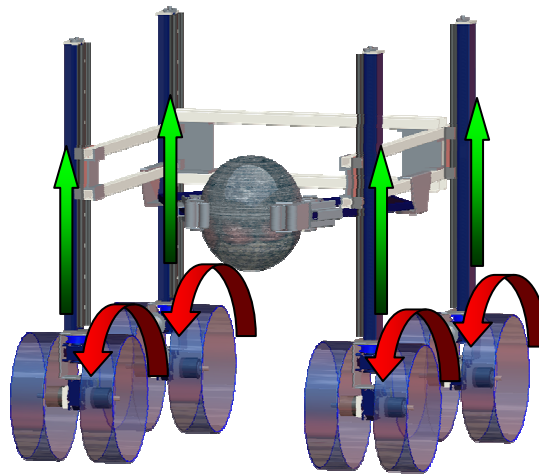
Sollevamento del carico e avanzamento del rover.
